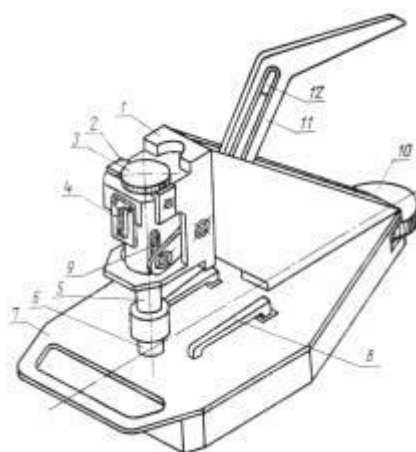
Прибор для измерения степени меления. 1 - корпус; 2 - скоба; 3 - регулировочный винт нагрузки; 4 - шкала; 5 - шток; 6 - резиновый пуансон; 7 - рабочий столик; 8 - зажимы образца; 9 - пружина; 10 - колесо регулировки зажимов; 11 - рукоятка; 12 - фиксатор рукоятки.
